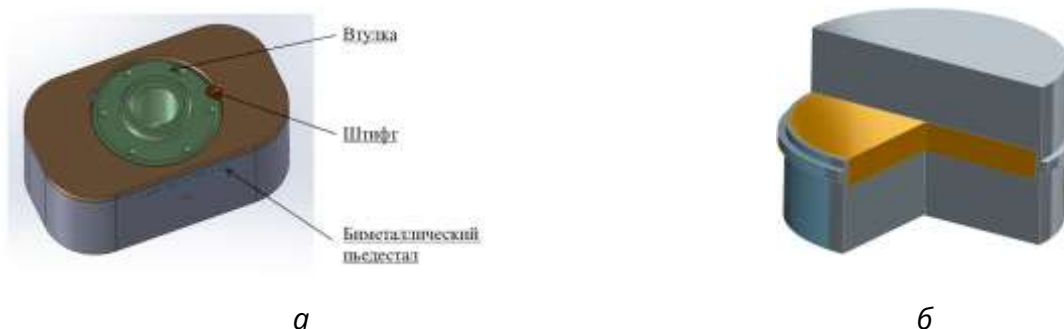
Пьедестал ЭС «модуль blankets/вакуумная камера» (а) и заготовка для ГИП (б)
